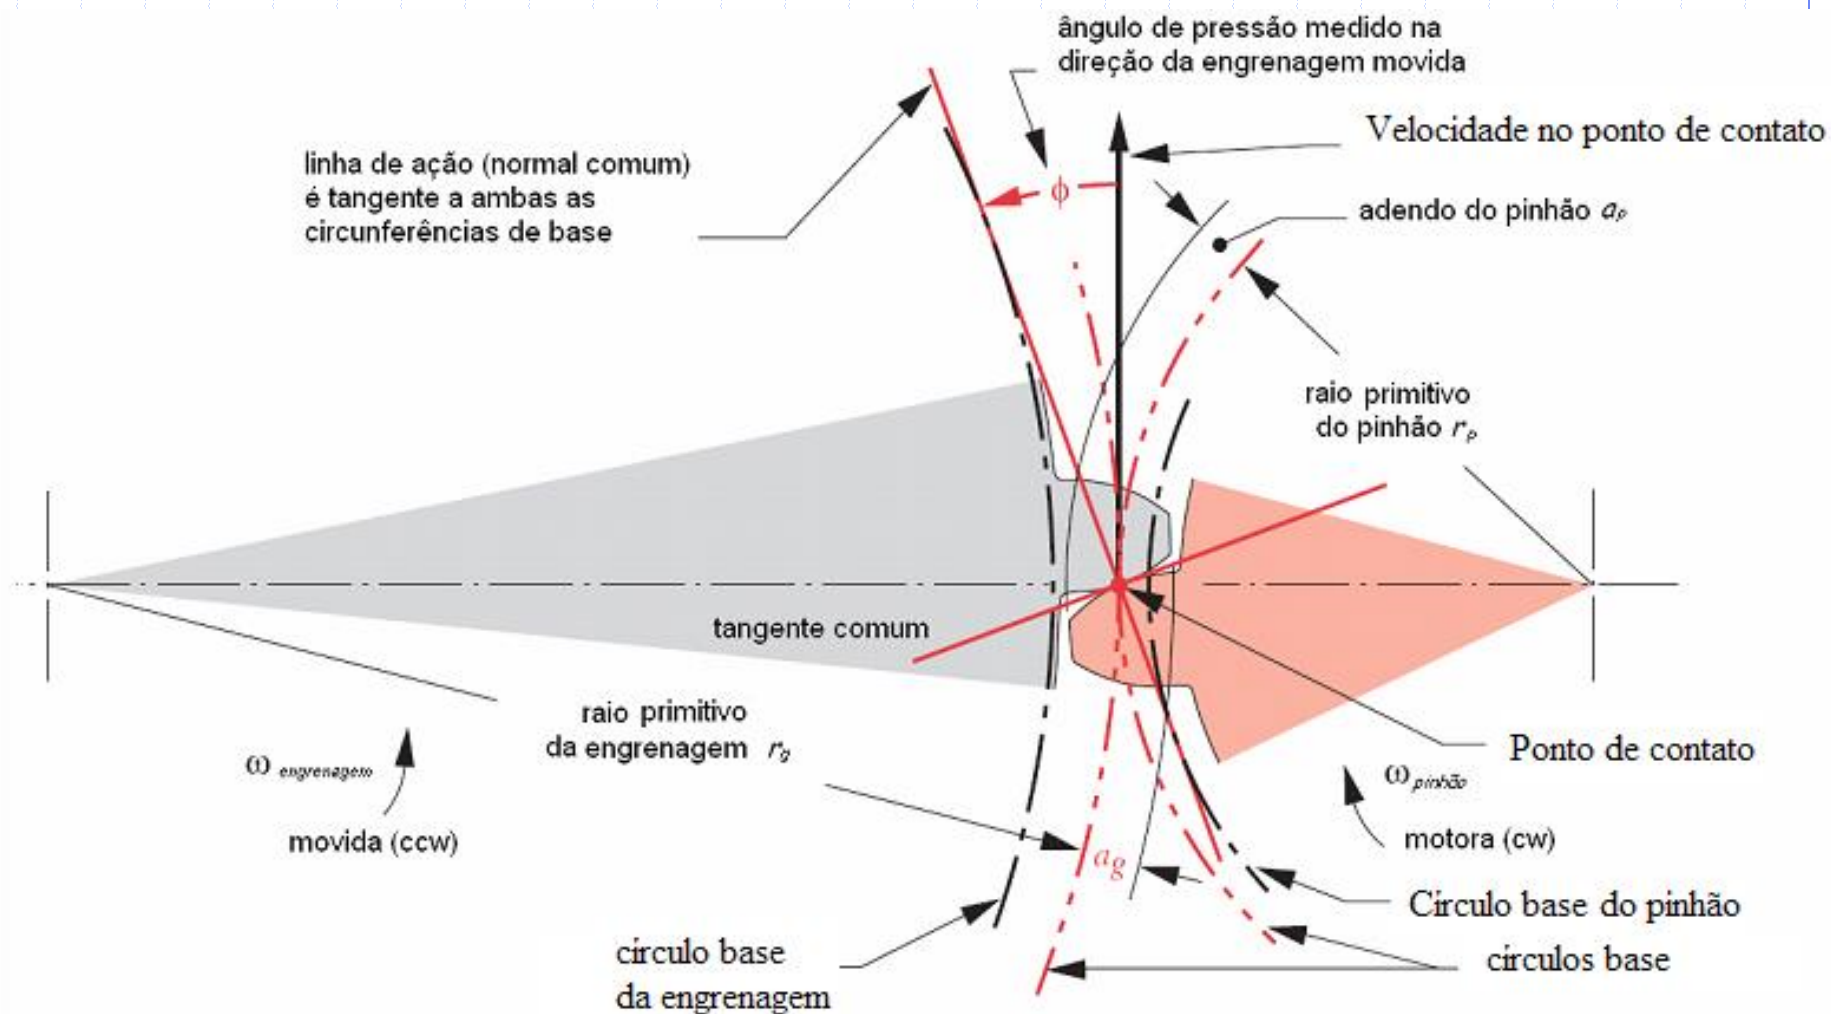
Geometria do Contato nos dentes das engrenagens.
